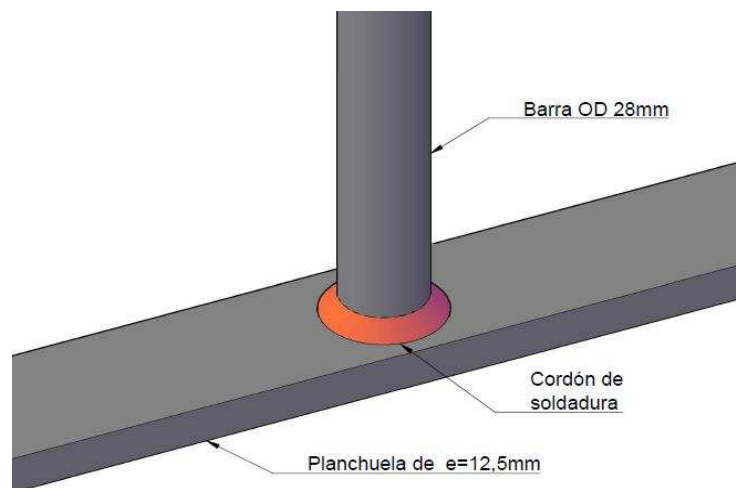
Perspectiva de unión soldada en extremo inferior de la estructura entre barra de acero de OD 28mm y planchuela de acero de espesor 12,5mm.
